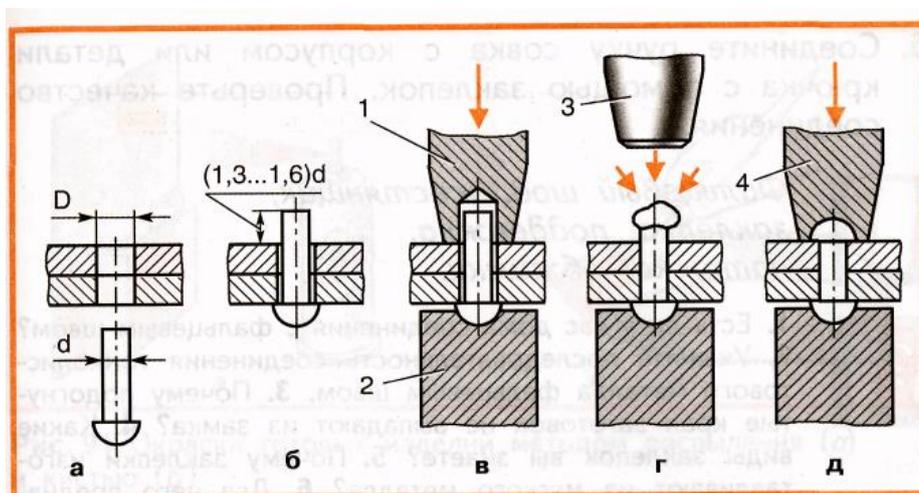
Этапы получения заклепочного соединения: а — сверление отверстий; б — размещение заклепки в отверстии; в — осаживание заготовок; г — расклепывание замыкающей головки; д — формирование замыкающей головки (1—натяжка; 2— поддержка; 3— молоток; 4— обжимка).
